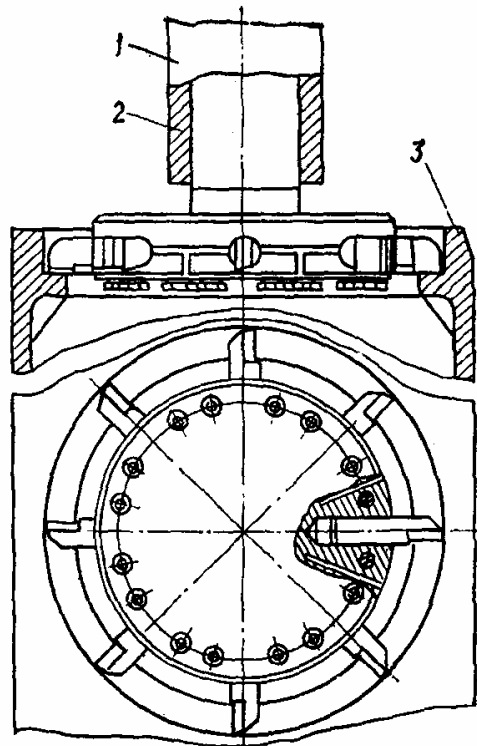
Багаторізнцева оправка для обробки виточок блока під бурти гільз циліндрів:
